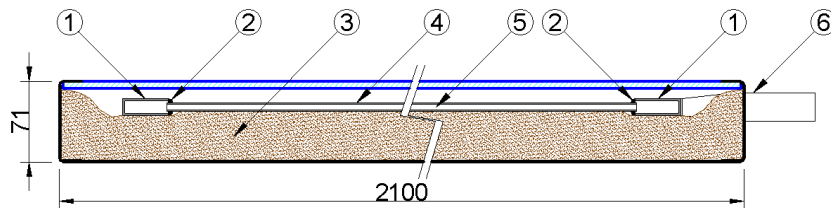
Corte longitudinal del prototipo diseñado. 1- Perfil U. 2- Soldadura. 3- Aislante. 4- Placa absorbidora. 5- Conducto circulación de fluido. 6- Tubo de salida del colector. Dimensiones en mm.
